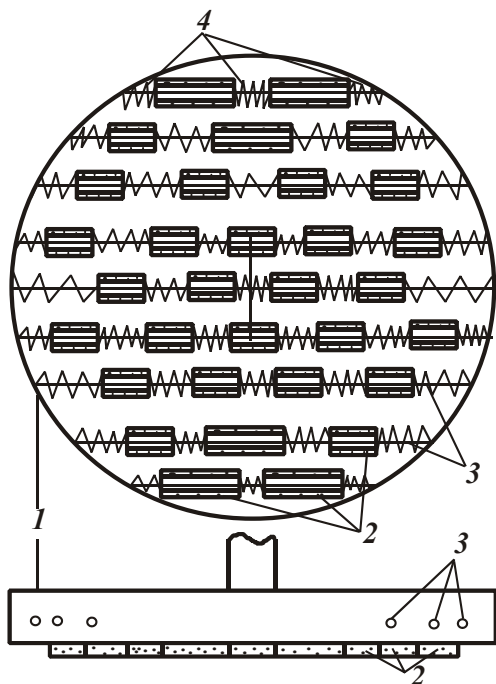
Инструмент для совместной обкатки и шлифования: 1 - корпус; 2 - круг-ролик; 3 - ось, на которой вращается круг; 4 - пружины.
